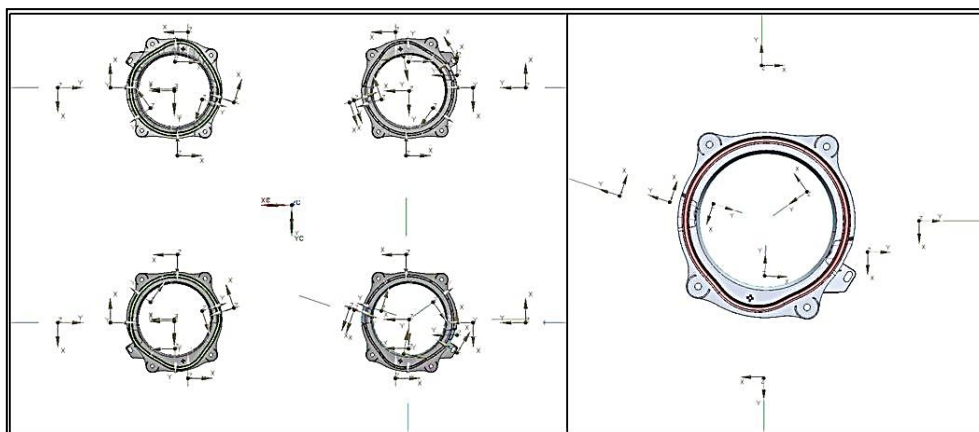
Eixos de desmoldagem no Molde IGM0705 completo e em Peça única
